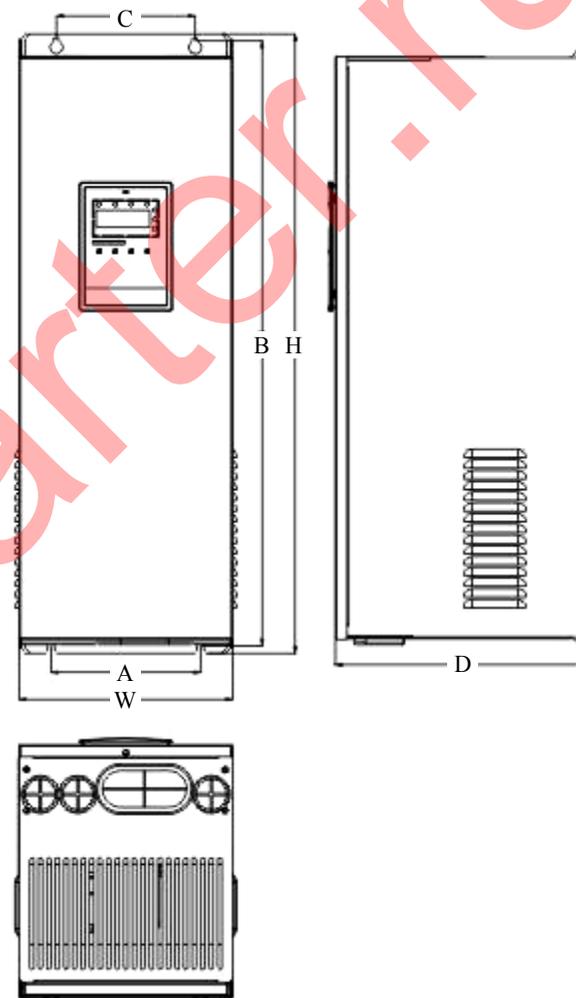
Габаритные и установочные размеры блоков торможения 380 В, 30 - 75 кВт
